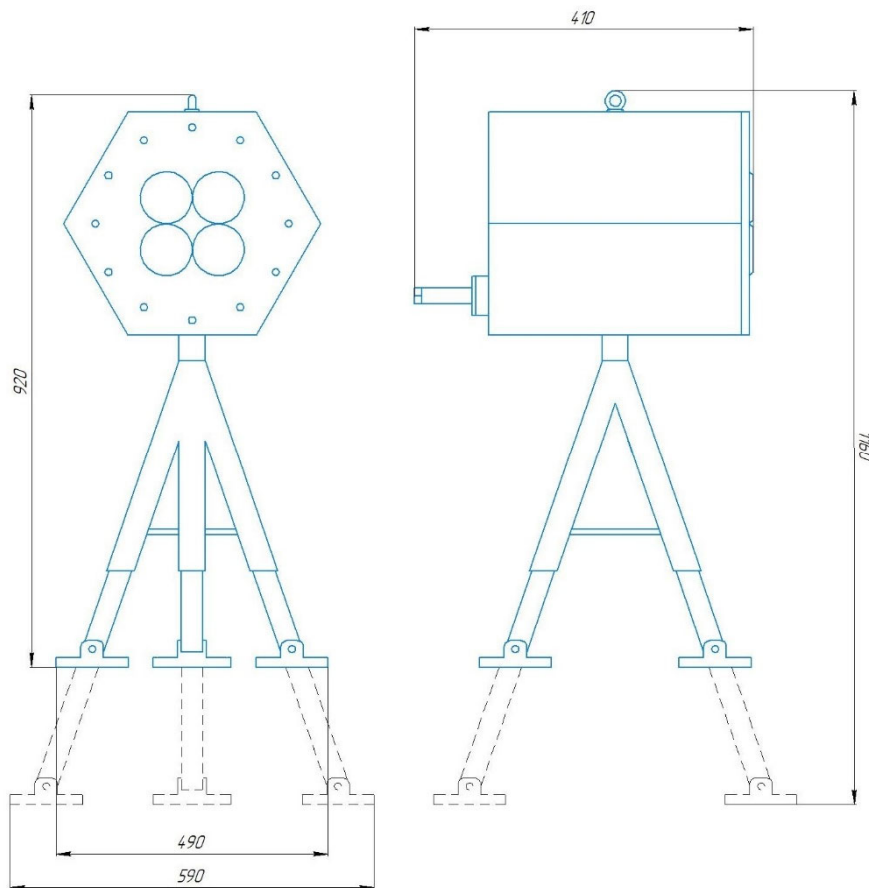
Габаритный чертёж СОПП серии К
